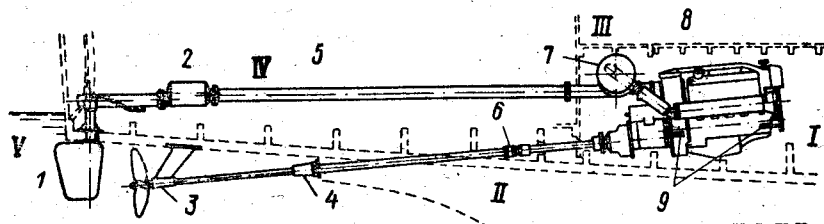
Активная борьба с шумом при установке двигателя. Глушение шума достигается следующим образом: I — эластичным креплением двигателя; II — эластичным креплением валопровода; III — установкой выпускного коллектора с глушителем; IV — охлаждением водой выпускного тракта; V — хорошим креплением руля, исключаяющим стук.
